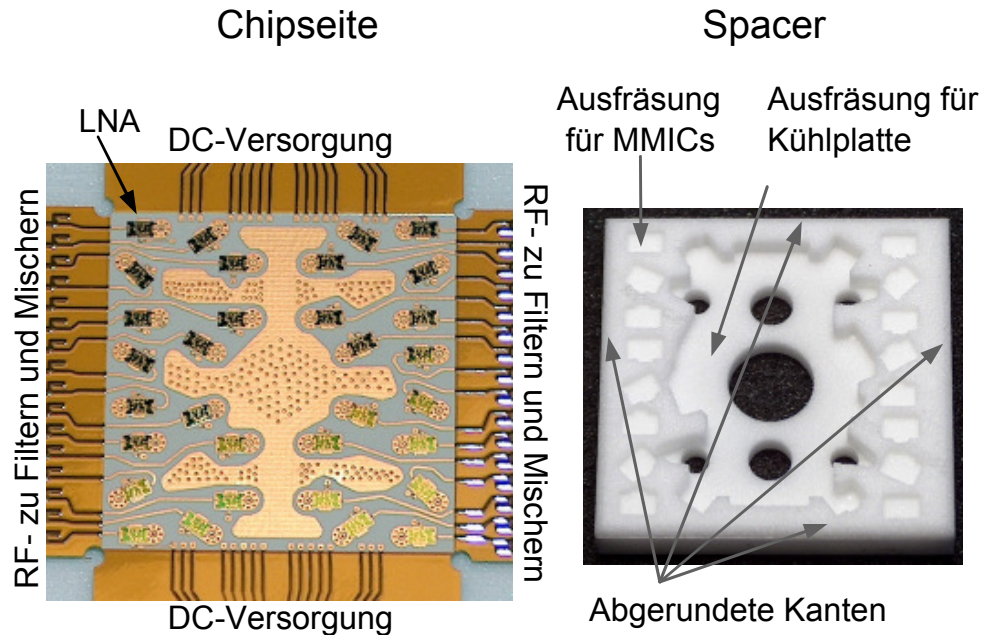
MMIC Packaging (links) und Rohacell Spacer (rechts) mit Ausfräsungen für MMICs und die Kühlung.
